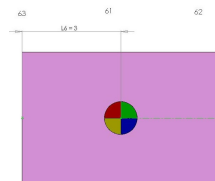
Imagen de la pieza 6 del mecanismo a-z-1133
